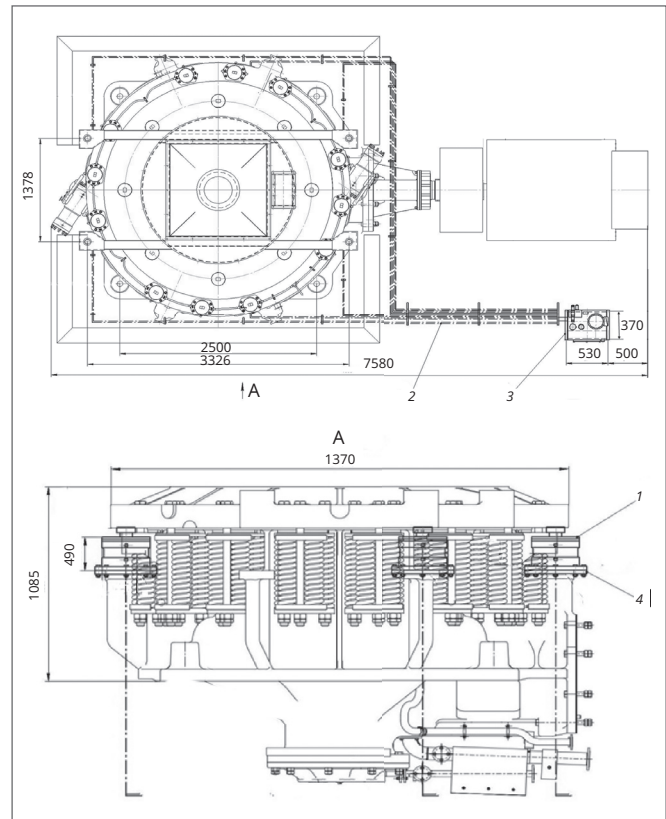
Схема установки гидростанции механизма подъема опорного кольца дробилки: 1 – гидроцилиндр; 2 – трубопроводы; 3 – гидростанция; 4 – присоединительный фланец
